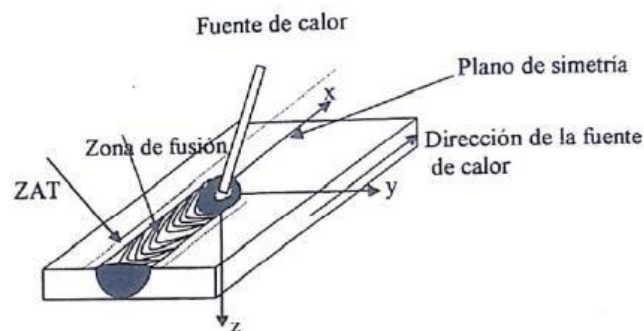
Diagrama de un proceso de soldadura.
